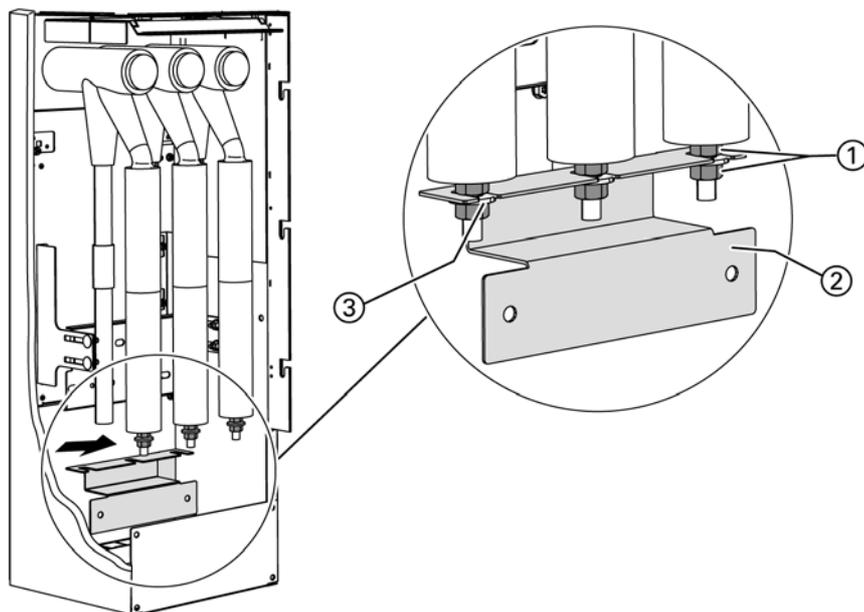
Вдвинуть пластину разрядника ② между шестигранными гайками M12 опор разрядника и затянуть гайки. Использовать шестигранные гайки M12 ① с пружинными шайбами ③.
